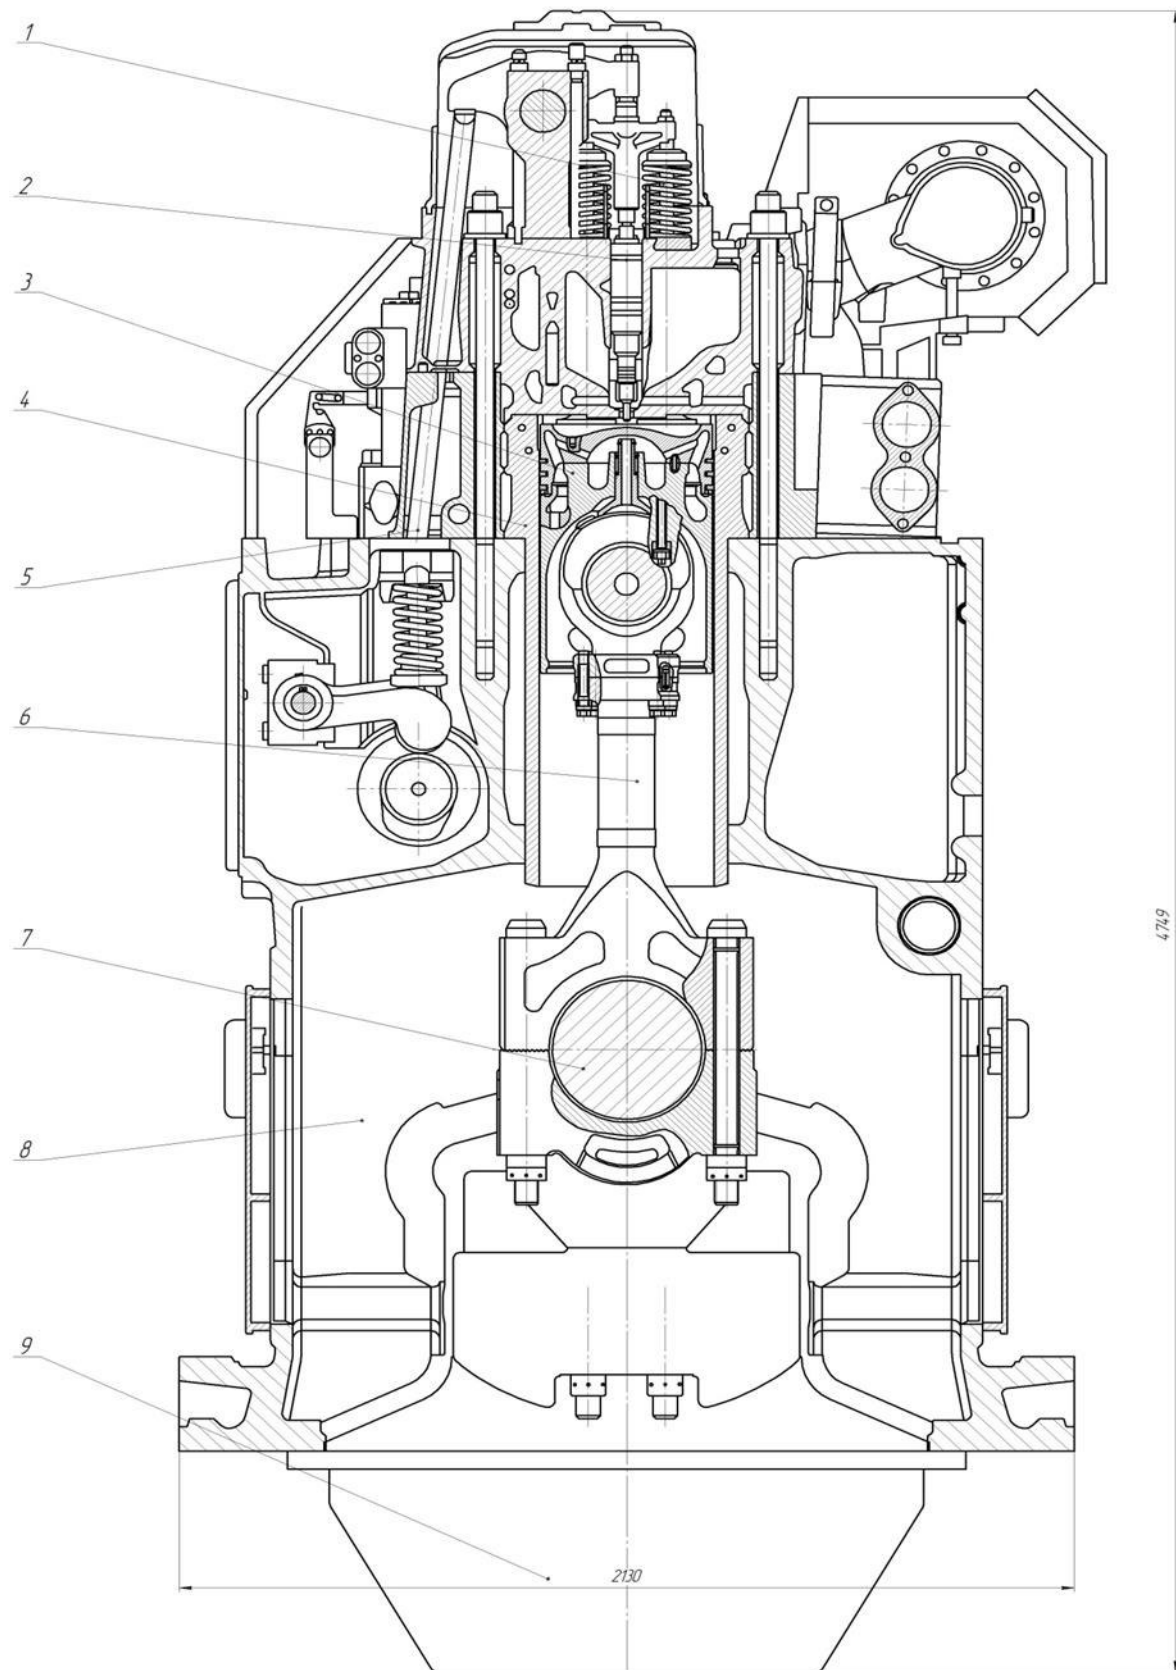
Поперечний переріз головного двигуна: 1 – клапан; 2 – паливна форсунка; 3 – поршень; 4 – циліндр; 5 – штовхач коромисла; 6 – шатун; 7 – колінчастий вал; 8 – картер; 9 – піддон картера
